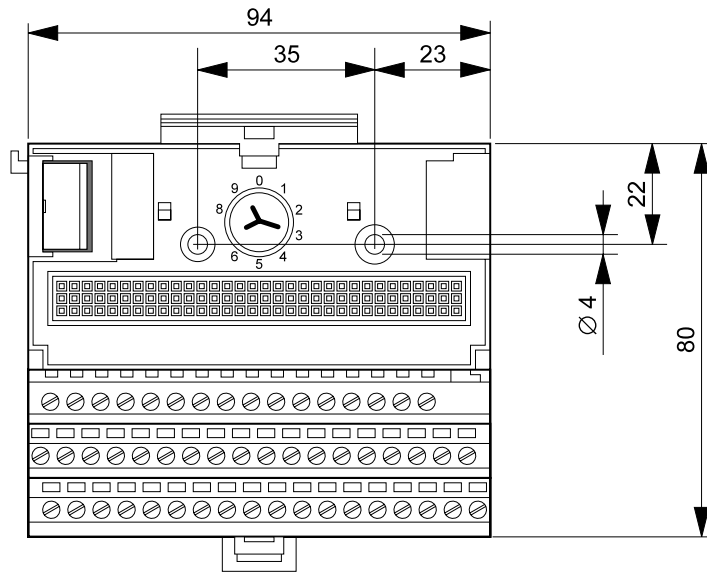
Befestigungsbohrungen für die Wandmontage
